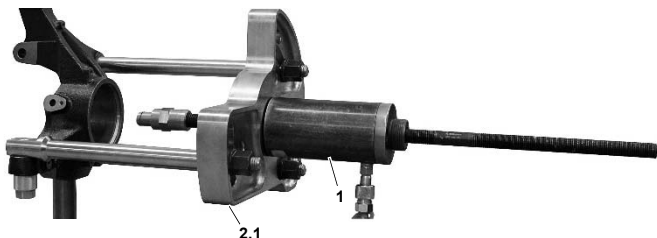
Aufnahmeadapter, Zentrierring und Druckring montieren. Radlager auf Zentrierring aufstecken.
